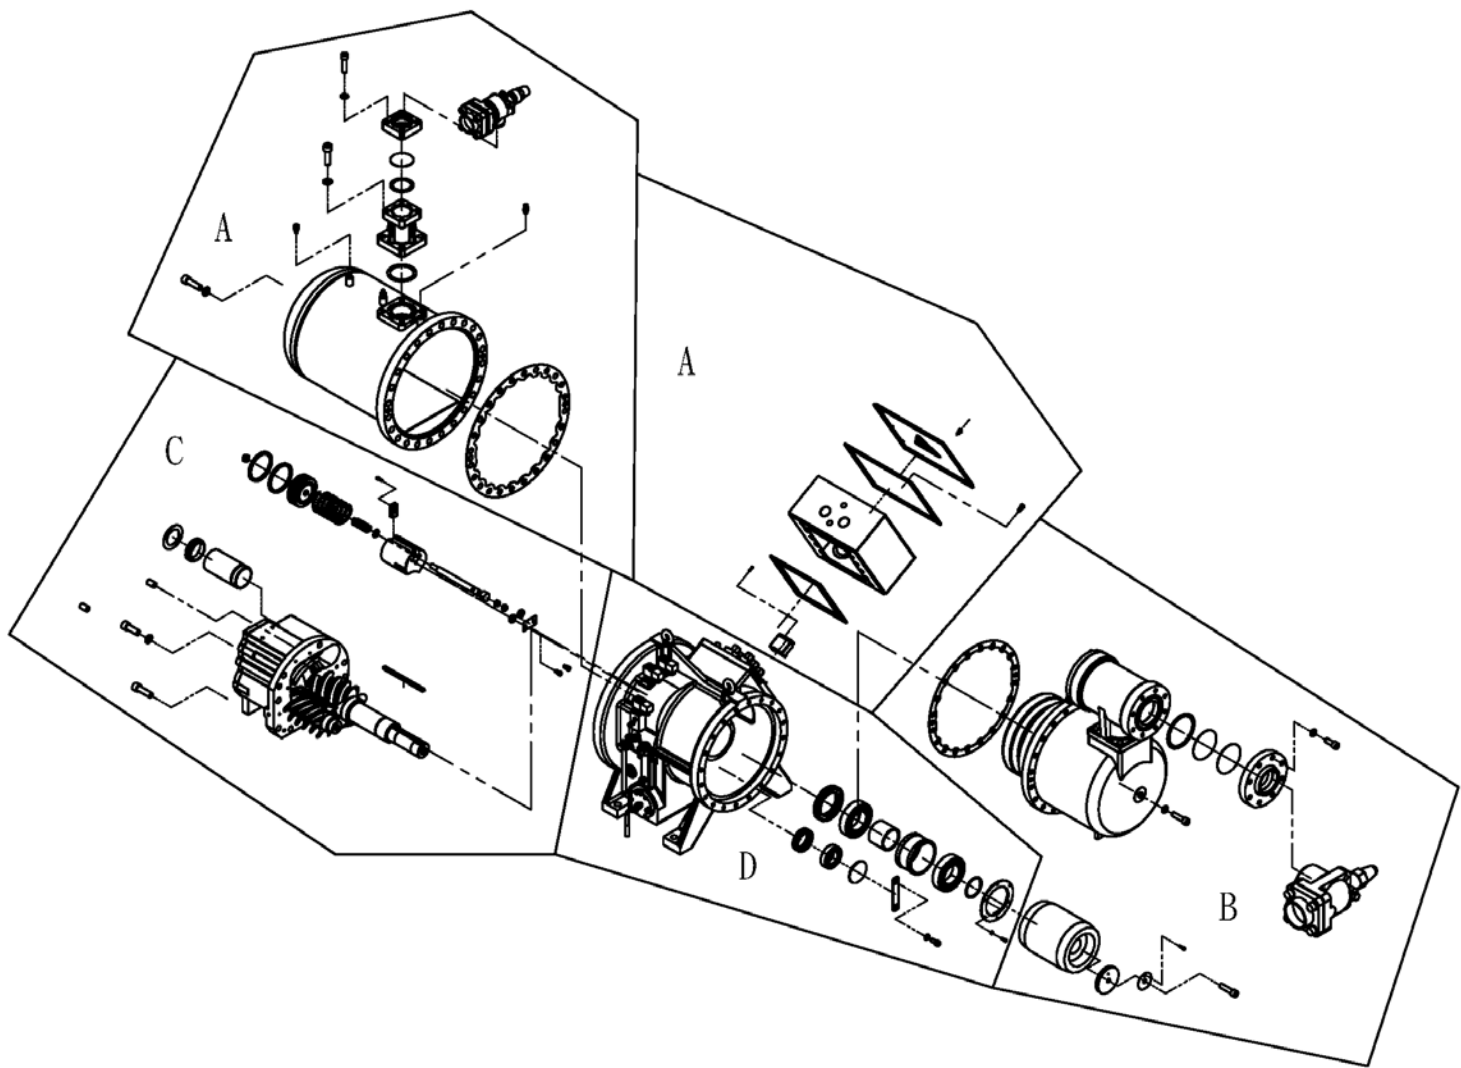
SR-4 (H) ~SR-7 (H) 分解說明/ Disassembly illustration
